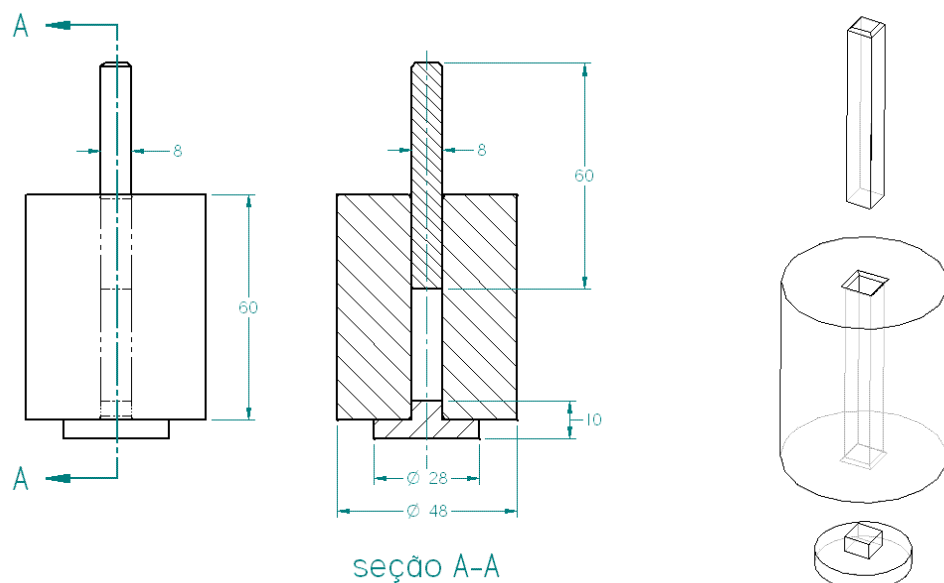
Dispositivo para a fabricação de corpos-de-prova para ensaios de dilatometria [mm]
